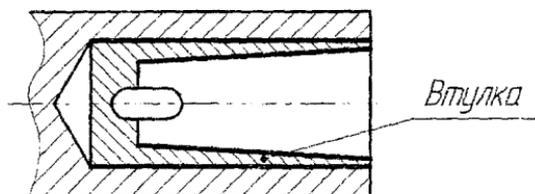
Восстановление конического отверстия шпинделя сверлильного станка
